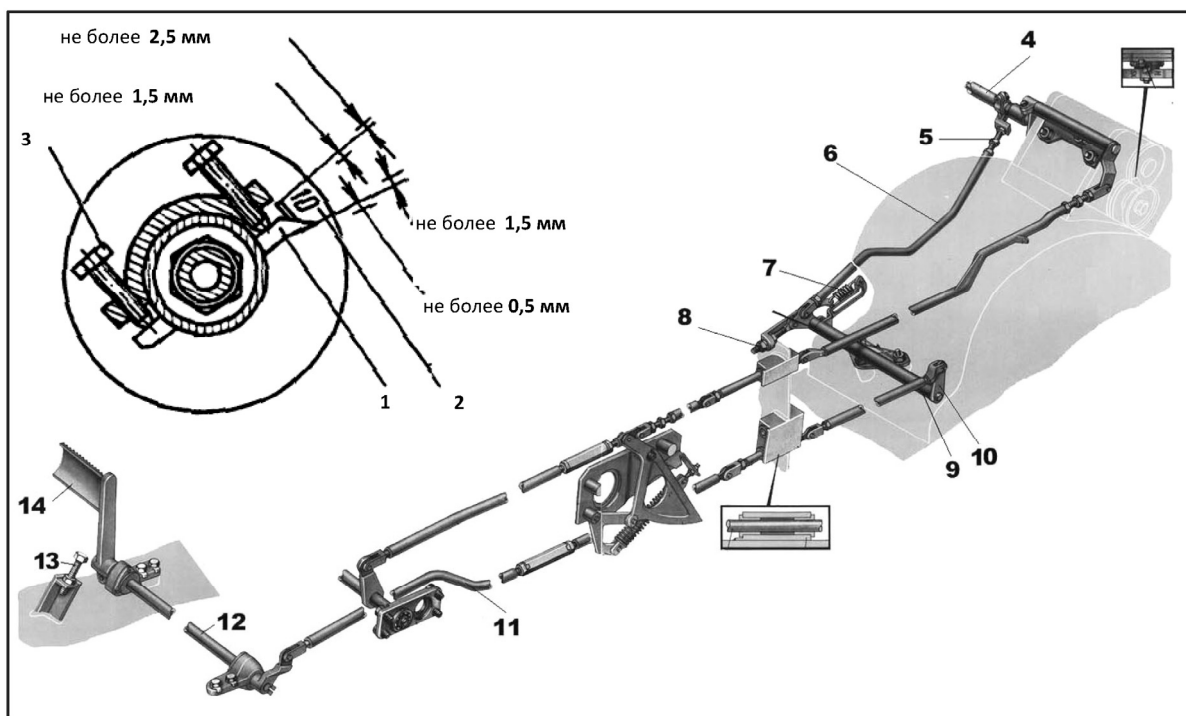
Привод выключения коробок передач (привод сцепления): 1 – стрелка; 2 – пластик; 3 – регулировочные болты; 4 – вал сцепления; 5 – стяжка; 6 – наклонная тяга; 7 – возвратная пружина; 8 – втулка; 9 – задний поперечный валик; 10 – рычаг; 11 – продольная составная тяга; 12 – передний поперечный валик; 13 – упорный регулировочный болт; 14 – педаль сцепления
